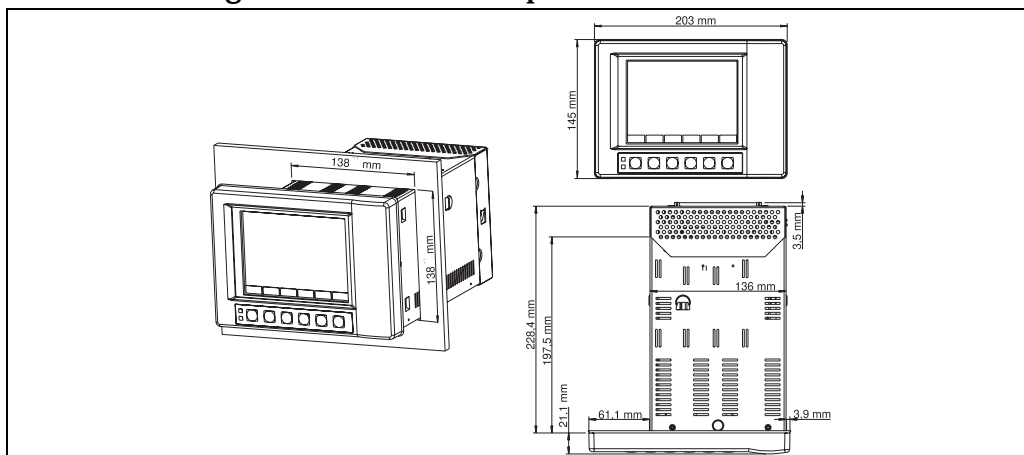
Montage en armoire de la version avec face avant en fonte moulée ou en inox
